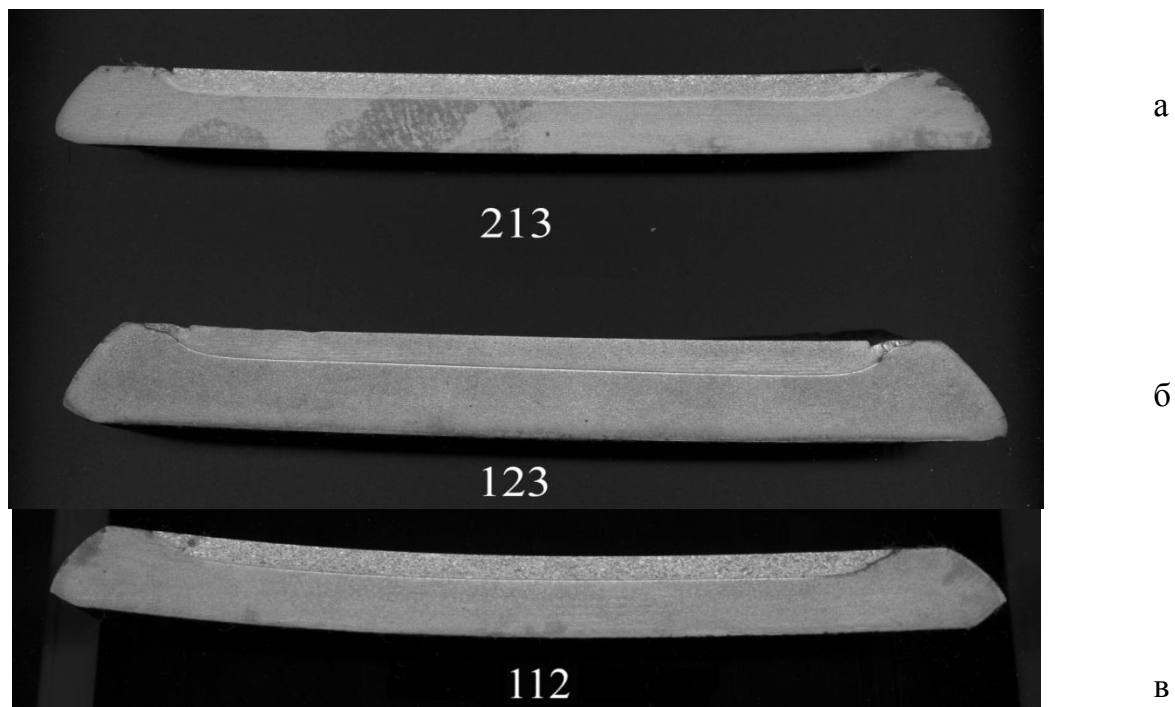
Общий вид в сечении образцов плакированной стали, полученных при помощи: а- пакетной прокатки; б - наплавки с последующей прокаткой; в - сварки взрывом с последующей прокаткой
